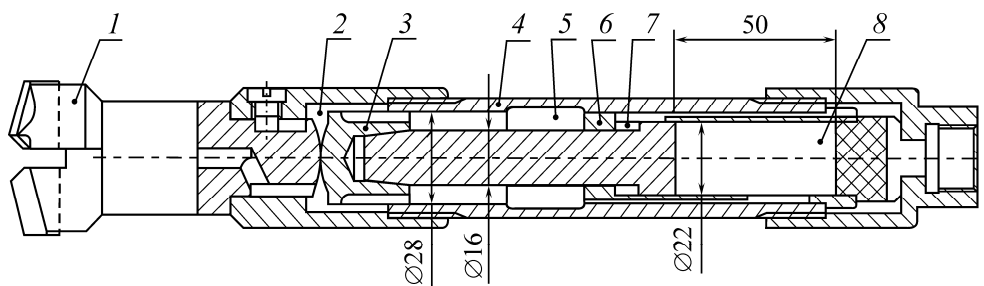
Модель погружного пневмоударника АШ-43: 1 — корпус; 2 — ударник; 3 — воздухораспределительная гильза; 4 — кольцевая полость камеры рабочего хода; 5 — торцевая камера рабочего хода; 6 — камера холостого хода постоянного давления; 7 — расточка; 8 — буровая коронка
